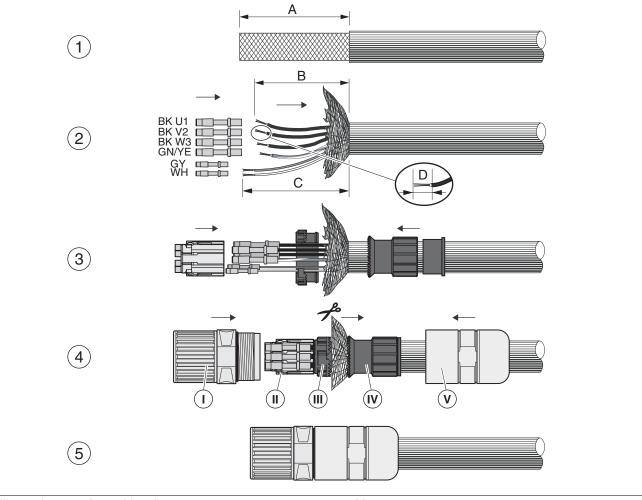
Assemblare il cavo motore con connettore motore M23
